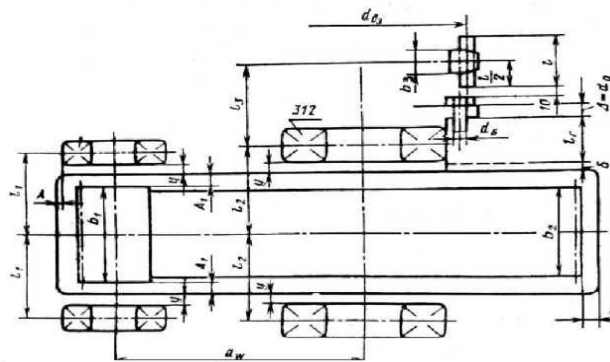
Схема предварительной компоновки одноступенчатого цилиндрического редуктора
